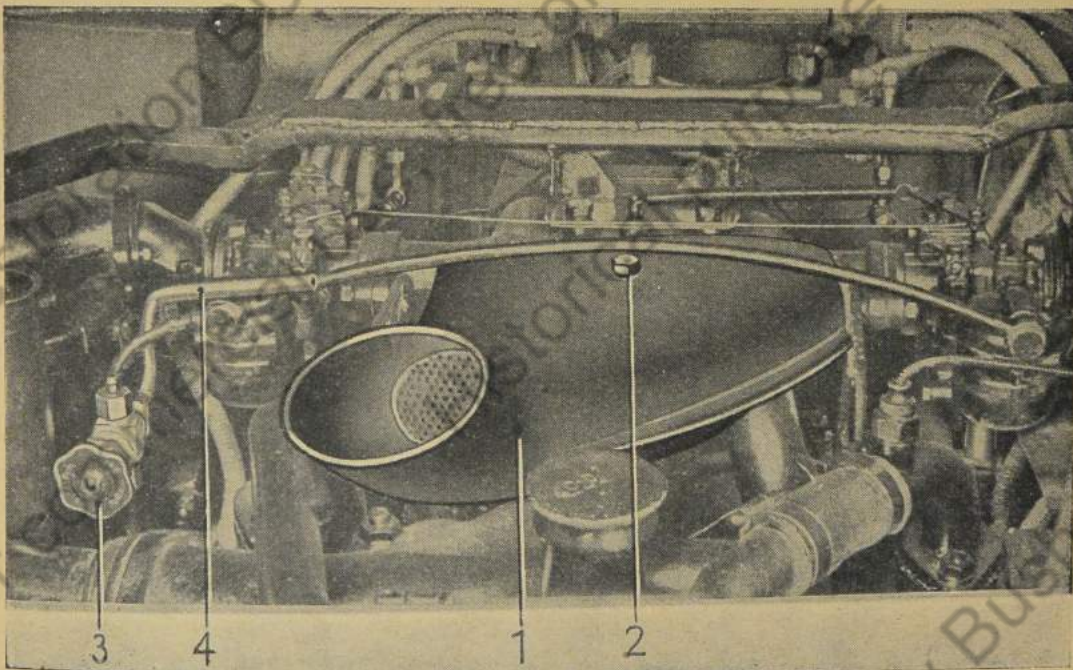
Heiztrichter für Saugrohr und Zweiweghahn eingebaut
